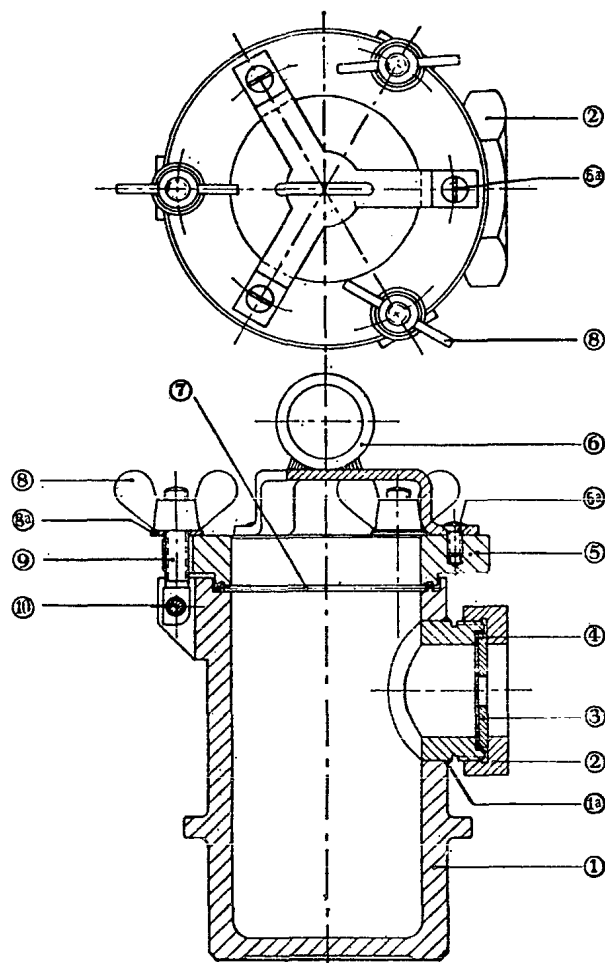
Recipiente a pressione, montato; schema in sezione verticale ed in pianta.
